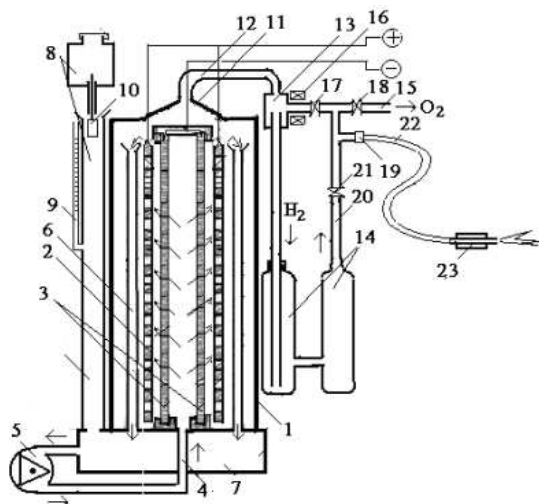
Водородный реактор для газовой резки и сварки металлов. Обозначения – по тексту.
